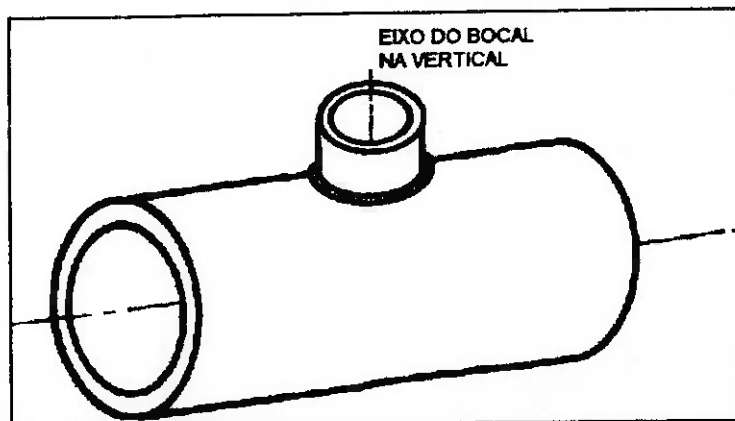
Posição de soldagem dos bocais e reforços a parede do vaso de pressão
